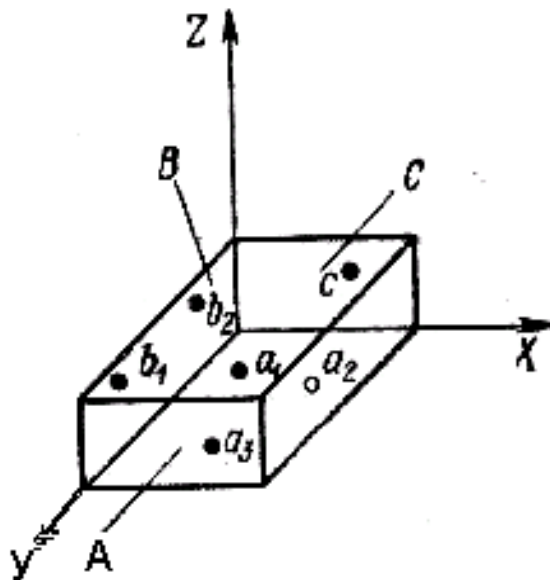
Базування призматичної заготовки в пристрої
